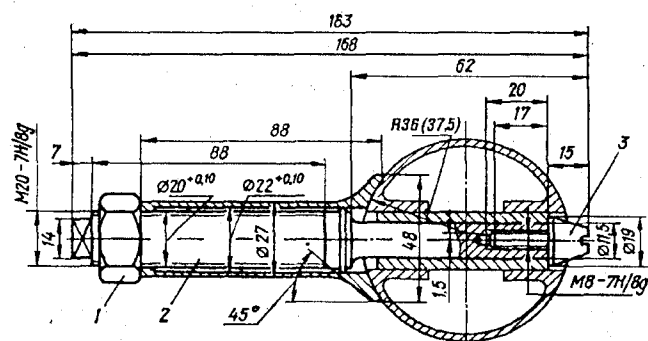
Приспособление для выпрессовки поршневого пальца: 1 – гайка; 2 – оправка; 3 – наконечник
